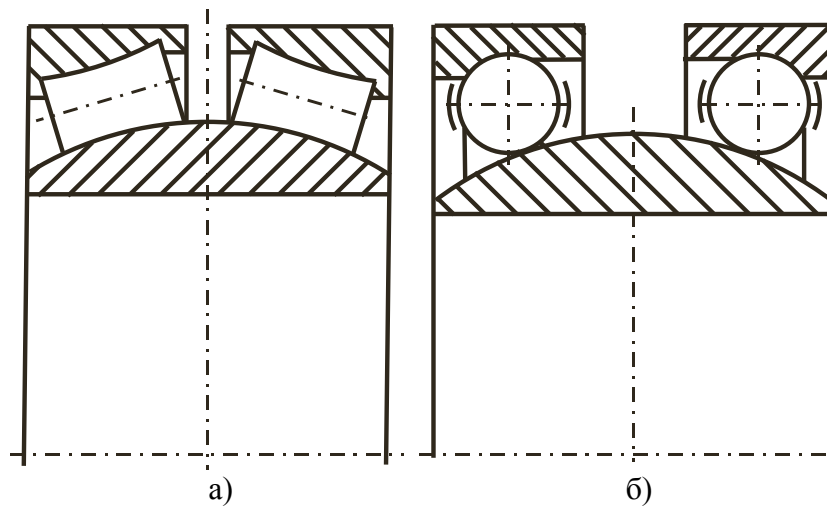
Конструкции двухрядных сферических подшипников качения.
